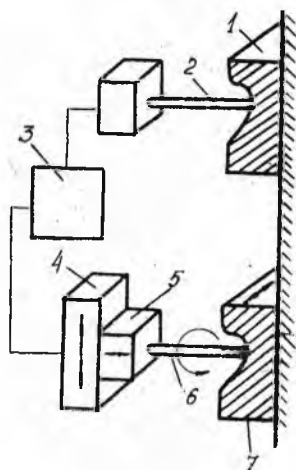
Изготовление штампа на копировально-фрезерном станке: 1 — модель; 2 — палец копировального устройства; 3 — электронное устройство; 4 — поперечина; 5 — шпиндельная бабка; 6 — пальчиковая фреза; 7 — штамп
